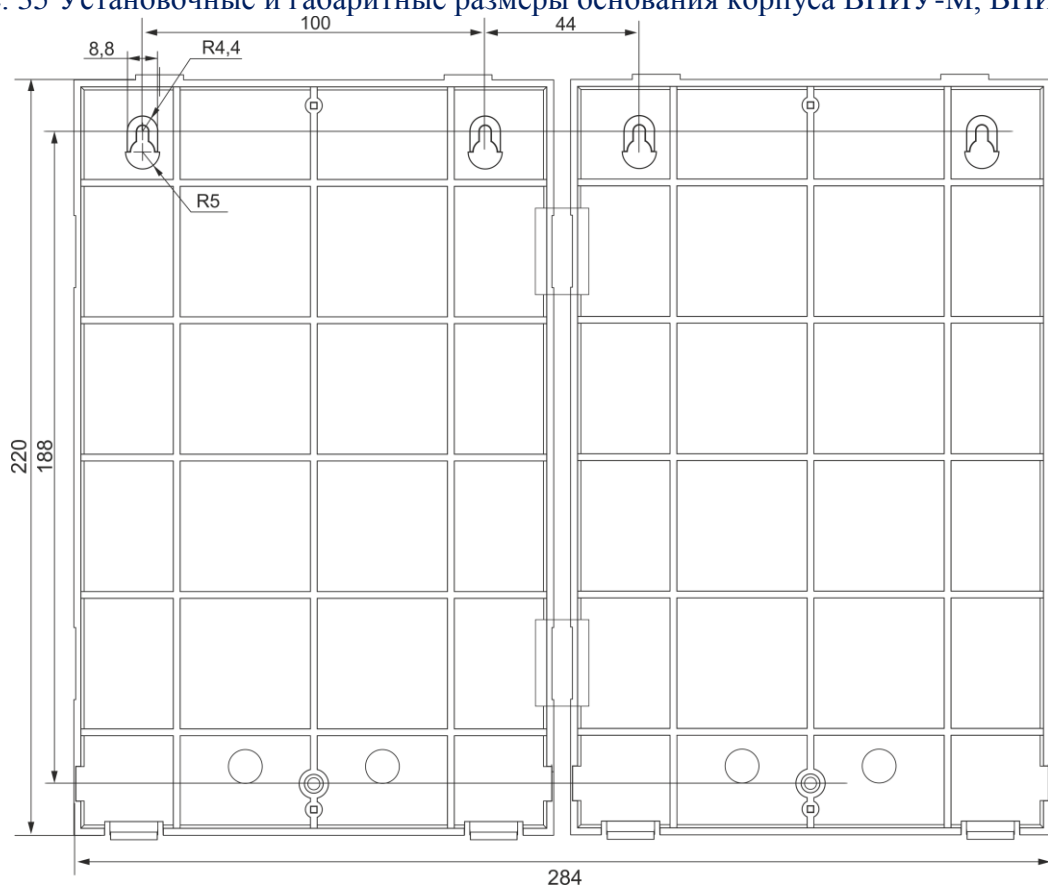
Установочные и габаритные размеры основания корпусов ВПИУ-М (или ВПИУ-Б) совместно с одной ВПИУ-Р или ВПИУ-А
